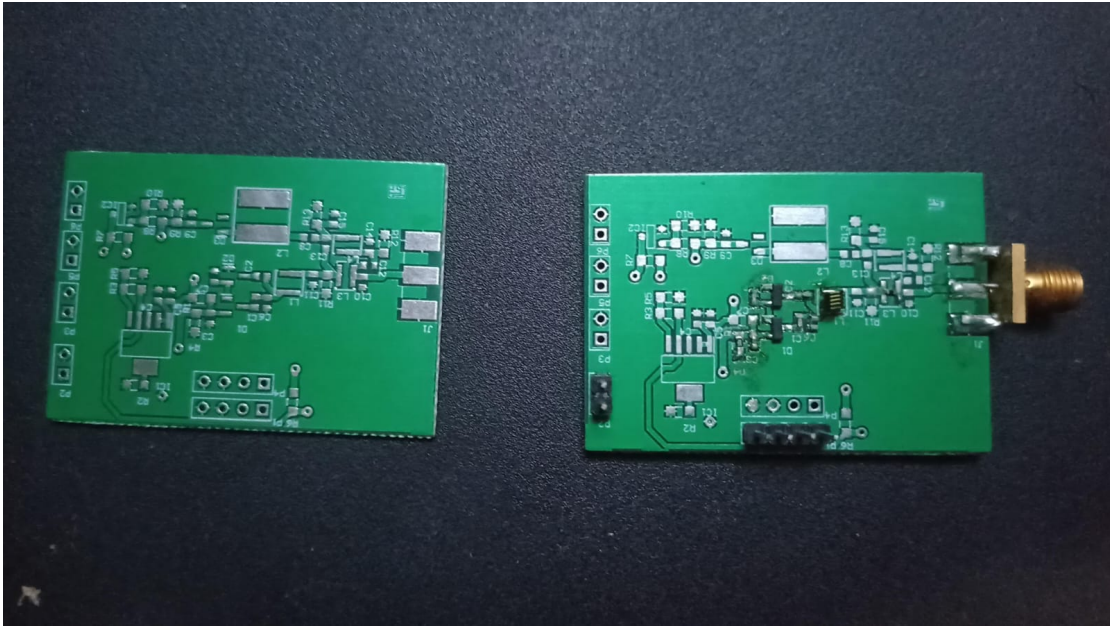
Placa de Circuito Impresso do retificador RF-DC: sem; e com os componentes eletrônicos soldados na placa.
